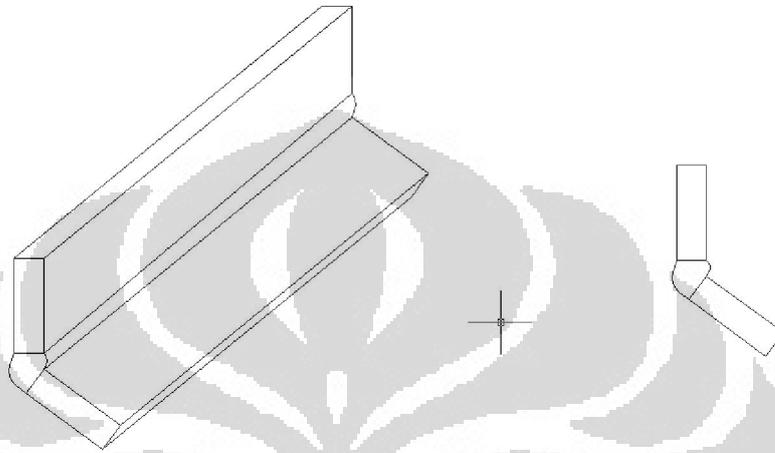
Profil L Buatan Hasil Welding
